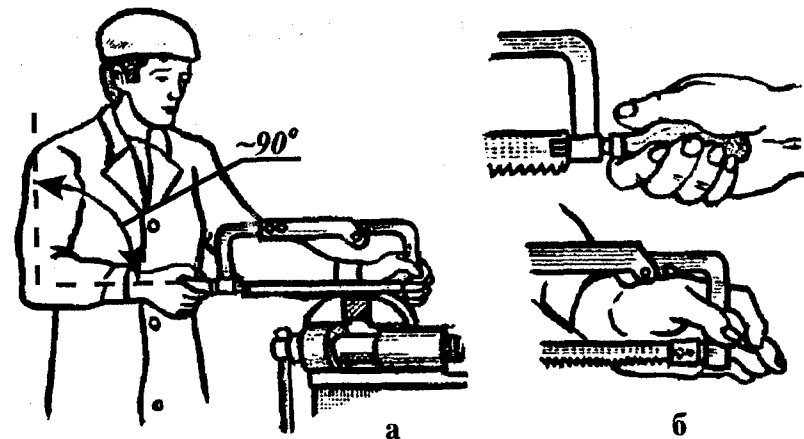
Работа ножовкой: а — положение корпуса; б — положение рук
